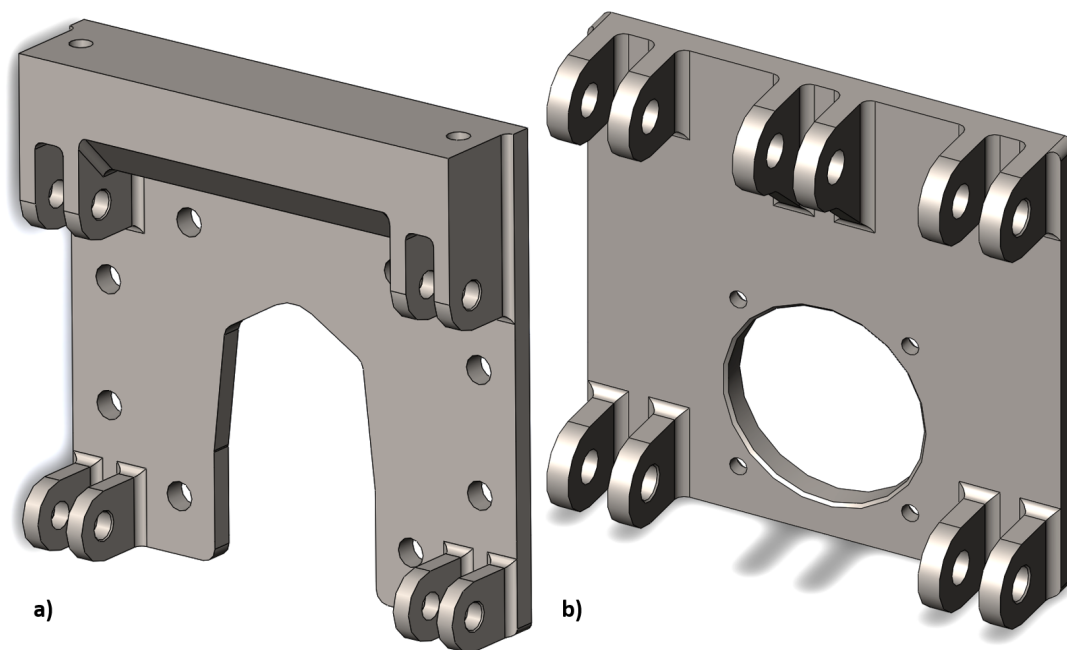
a) Placa Traseira b) Placa Frontal, do sistema original
